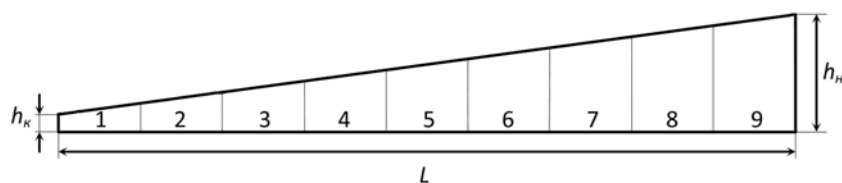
Схематичний вид клиноподібного зразка для моделювання умов гарячої деформації на прокатному стані «ДУО-280»:
